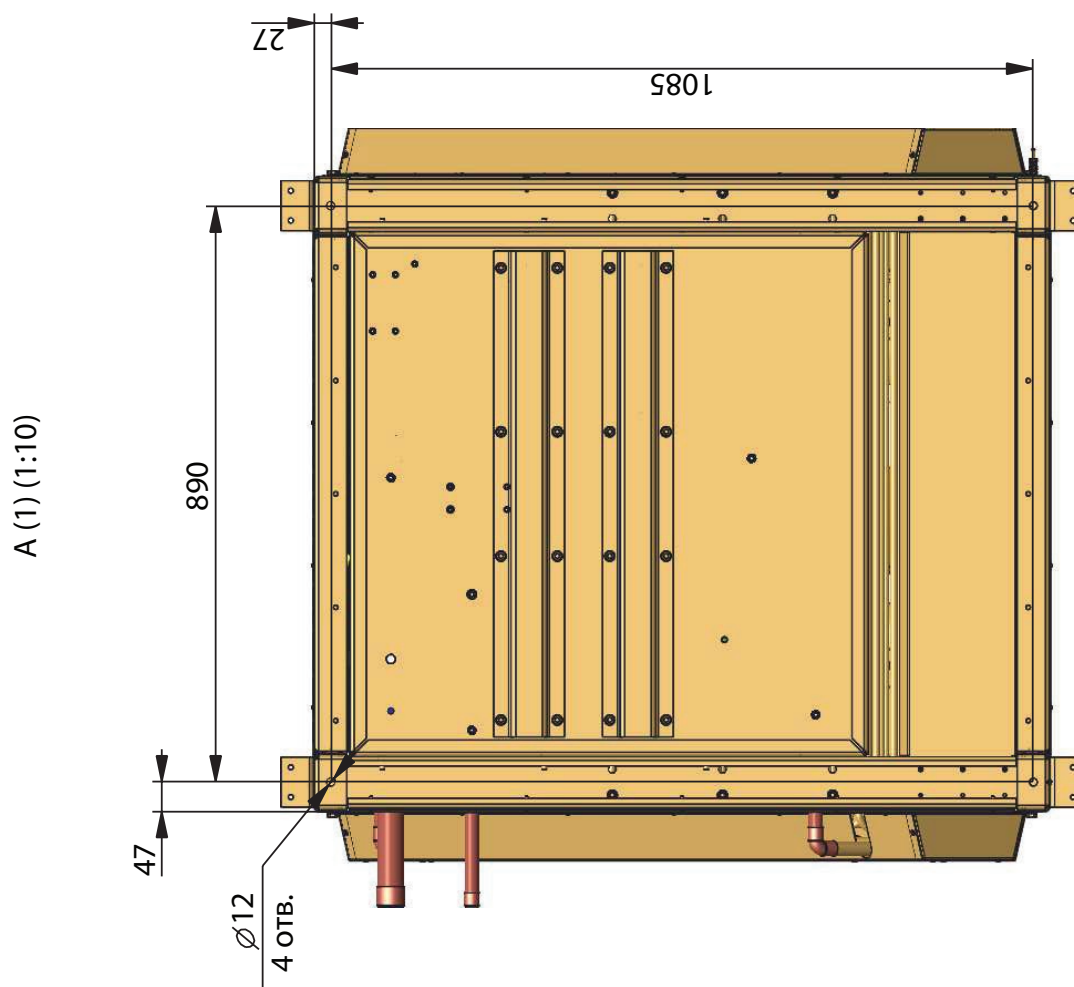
Агрегат компрессорный МАКК 120-241, -321, -401, -471
